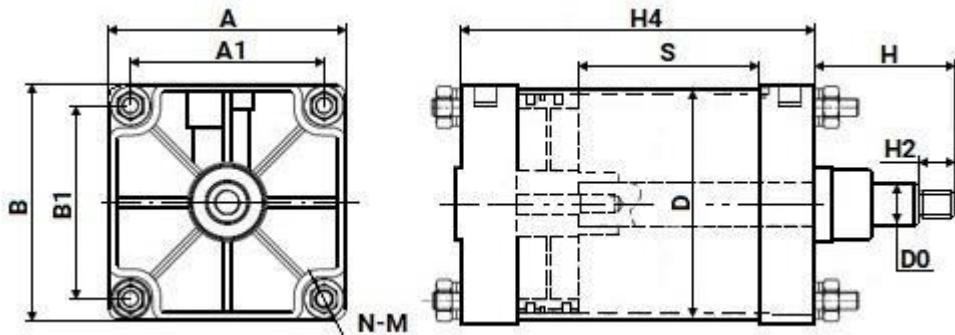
Размеры пневмоцилиндра SC 250x400
